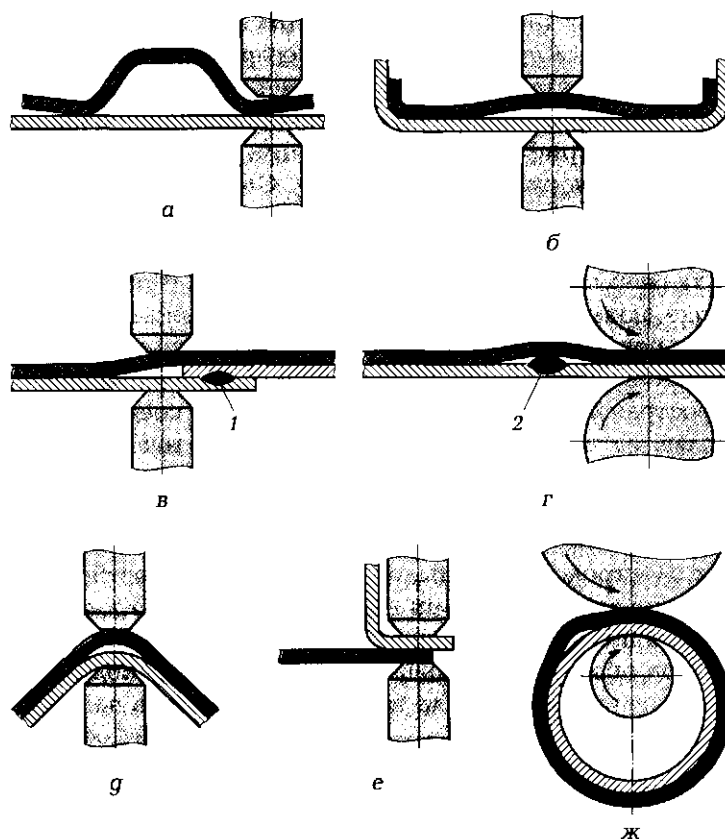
Дефекты подготовки и сборки деталей под сварку:
